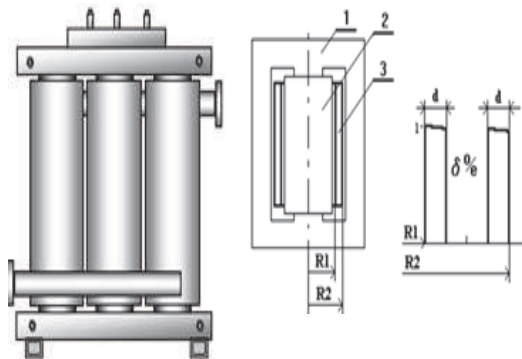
Схематичное изображение индуктивно-кондуктивного нагревателя и плотность тока в стенках цилиндрической камеры нагрева из алюминия
